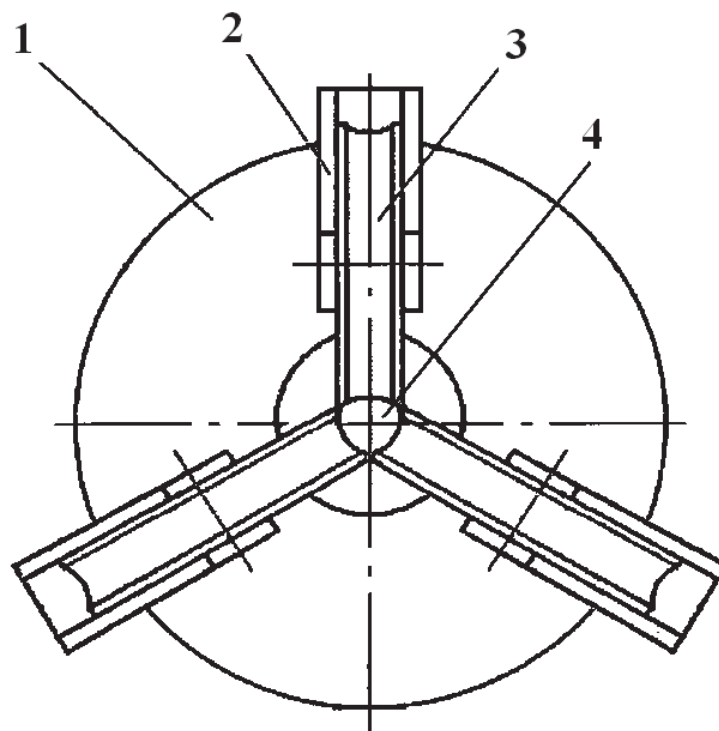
Приспособление для проведения волочения на токарном станке в трёхкулачковом патроне: 1 – патрон; 2 – кулачок; 3 – ролик; 4 – изделие
